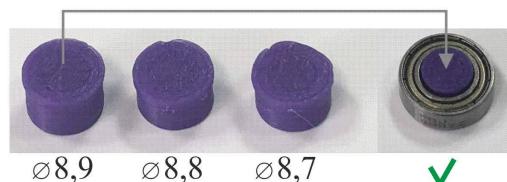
Тестовая печать для подбора диаметра оси шкива
